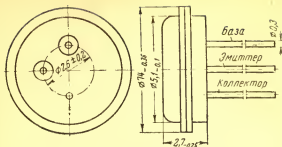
Габаритный чертеж транзисторов 2Т301—2Т301Ж.
